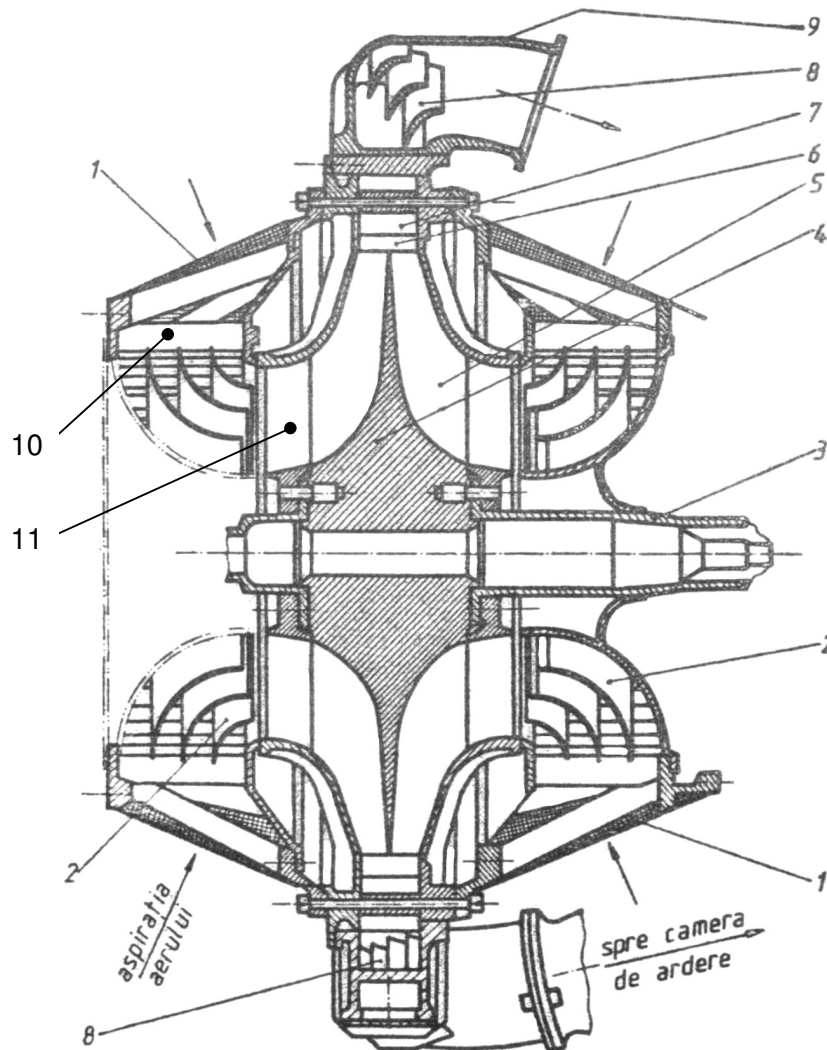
Compresorul centrifug al motorului turboreactor de aviație RD-45 [16]: 1 - grătar de protecție la aspirație; 2 - palete directoare fixe, pentru direcționarea aerului aspirat; 3 - arborele motorului; 4 - disc de bază; 5 - palete rotorice; 6 - difuzor nepaletat; 7 - difuzor paletat; 8 - palete directoare în canalul de legătură dintre compresor și camera de ardere; 9 - galeria de refulare spre camera de ardere; 10 - aparat director fără palete (neted); 11 - aparat director mobil
